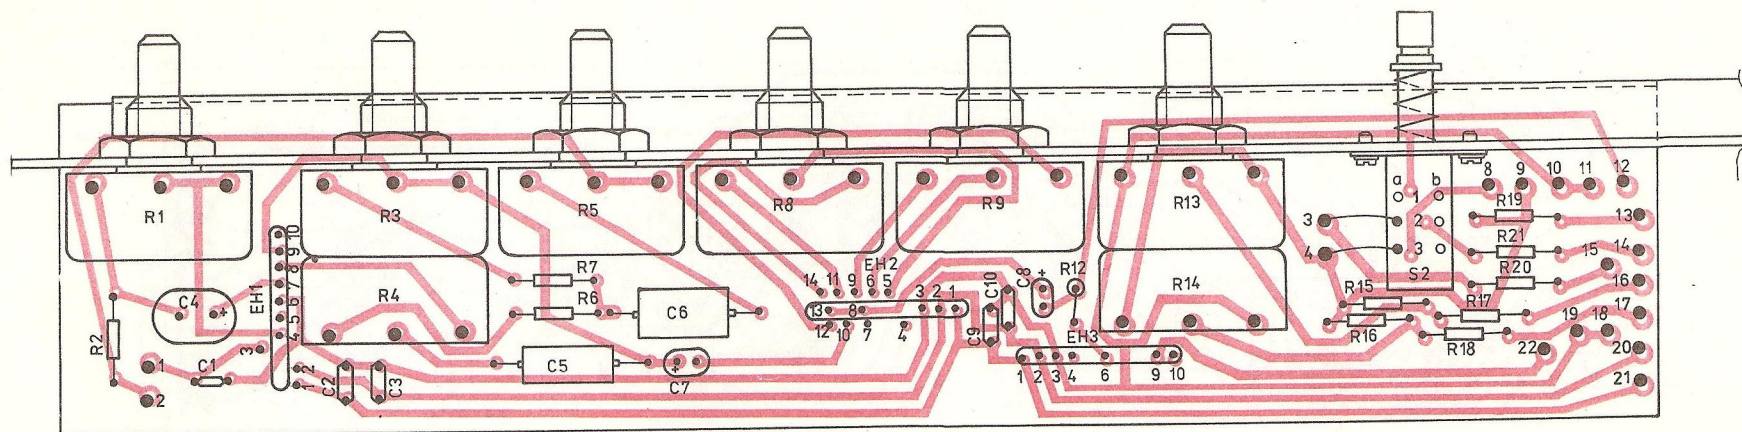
Schéma zapojení desky směřovací 3AK 061 39
